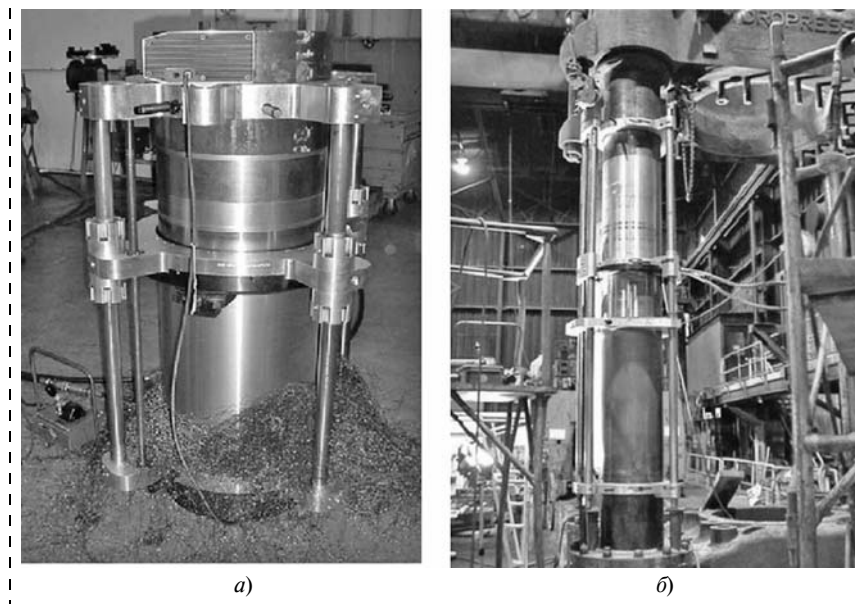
Примеры применения расточного оборудования при восстановлении цилиндрических поверхностей центральной цапфы экскаватора ЭШ-10.70 (а) и штока вспомогательного цилиндра механизма шагания экскаватора ЭШ-15.90 (б)
